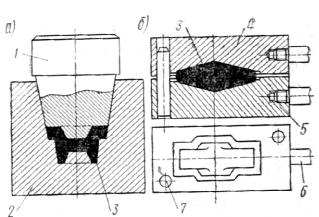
Конструкция подкладных штампов для закрытой штамповки втулки (а) и открытой штамповки коромысла (б):
